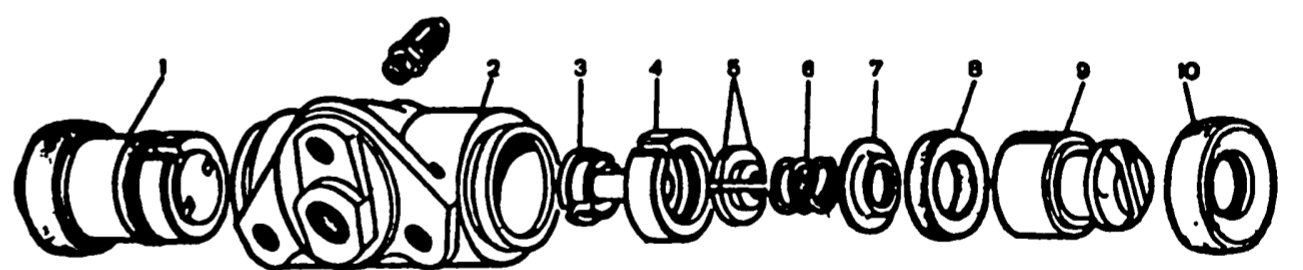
Детали колесного цилиндра: 1 - поршень в сборе; 2 - корпус цилиндра; 3 - упорный винт; 4 - упорное кольцо; 5 - сухари; 6 - пружина; 7 - опорная чашка; 8 - уплотнитель; 9 - поршень; 10 - защитный колпачок
